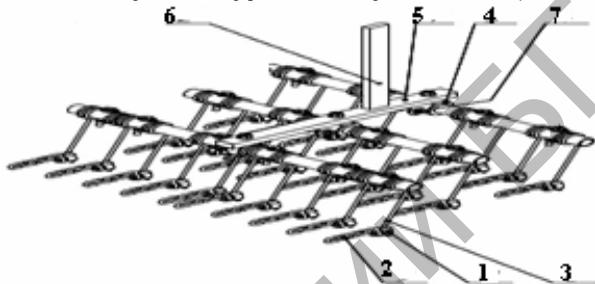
Пружинный рыхлитель (вид сверху)
